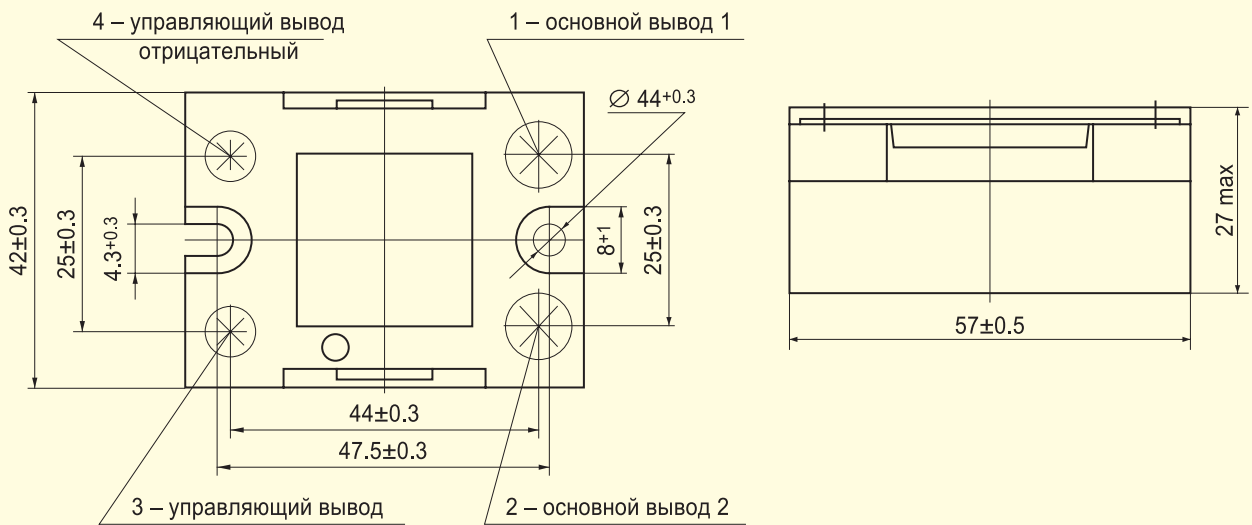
Габаритно-присоединительные размеры модуля МТСО15/18
